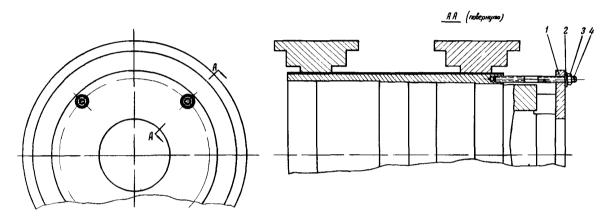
Приспособление для снятия контактных колец турбогенератора ТВВ-320-2 (выкопировка с чертежа завода "Электросила" № 5БС-487-059):
